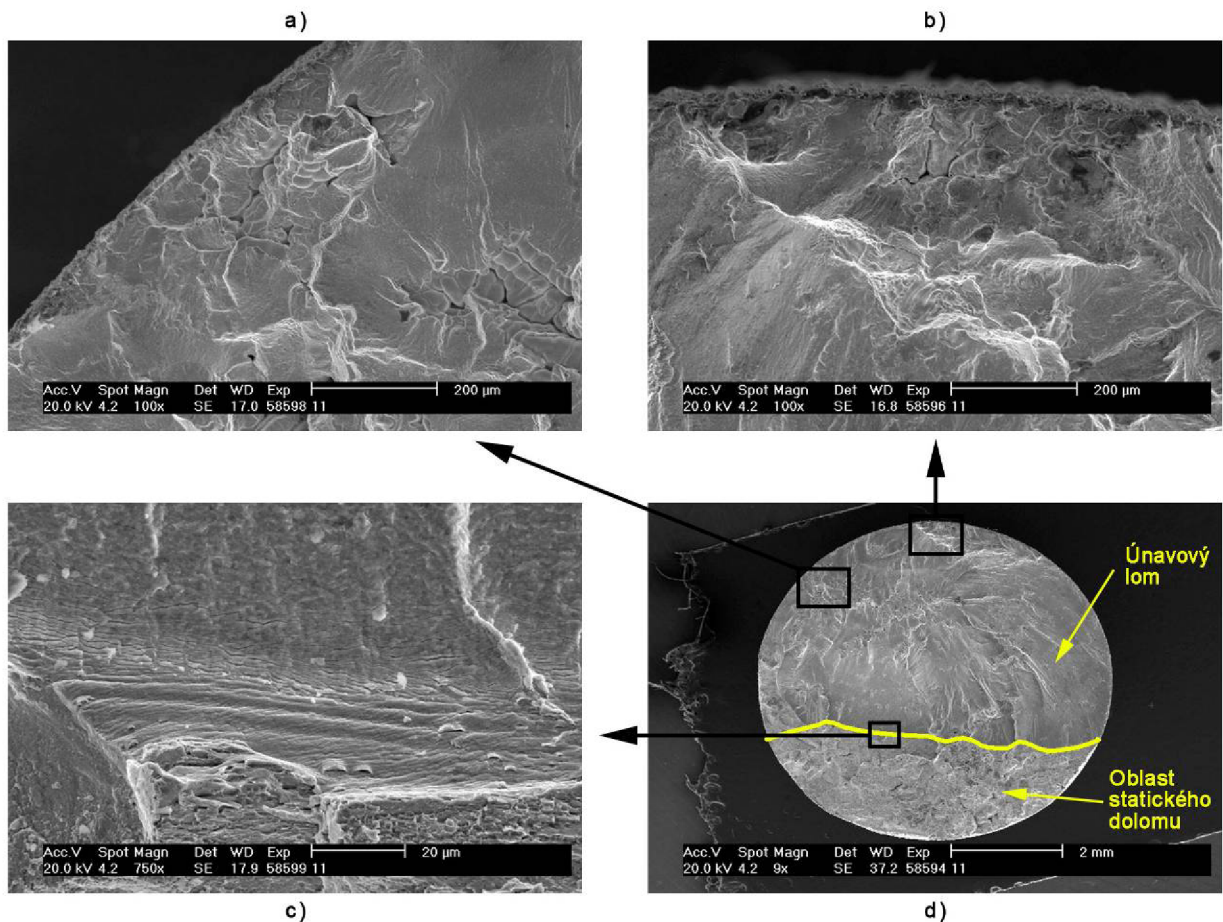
a) Detail řediny na okraji vzorku 7 - iniciace únavové trhliny (REM),
